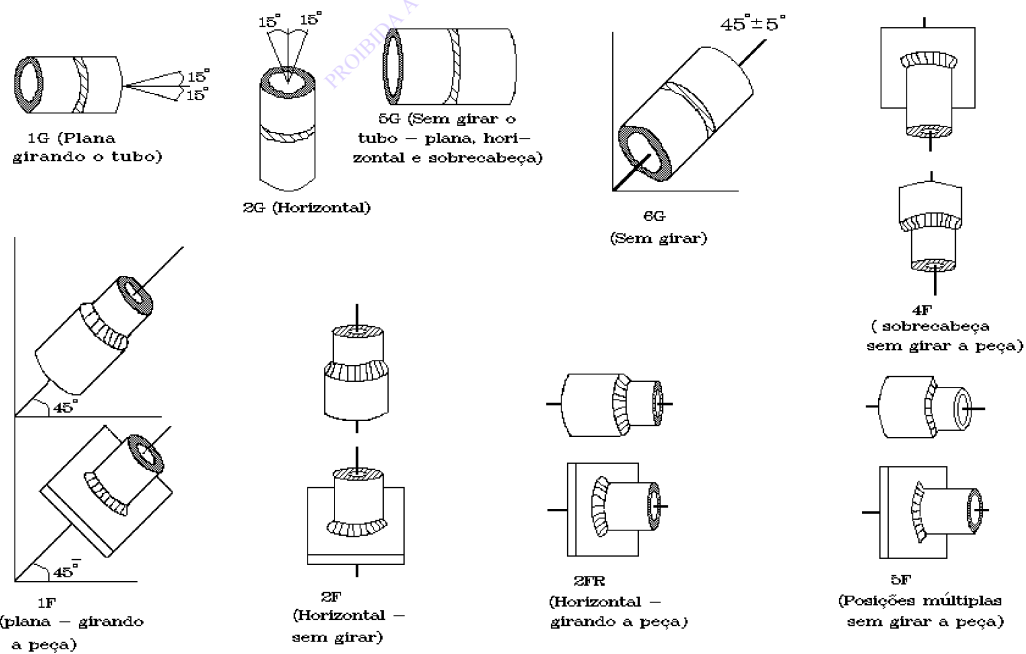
Posições de Soldagem para Tubos Convencionadas pela ASME.
